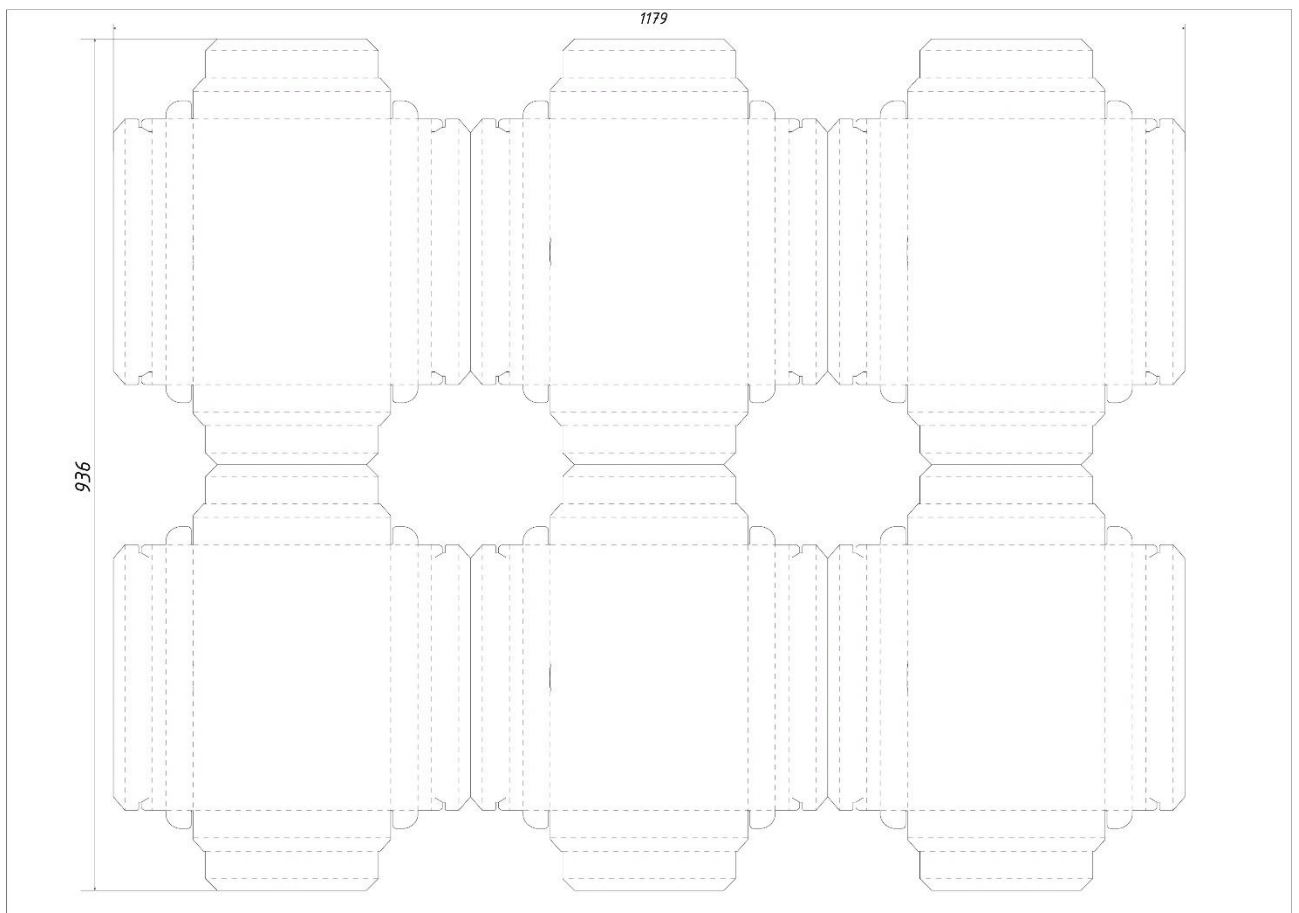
Розгортки корпусу упаковки розміщені на аркуші картону формату B0
